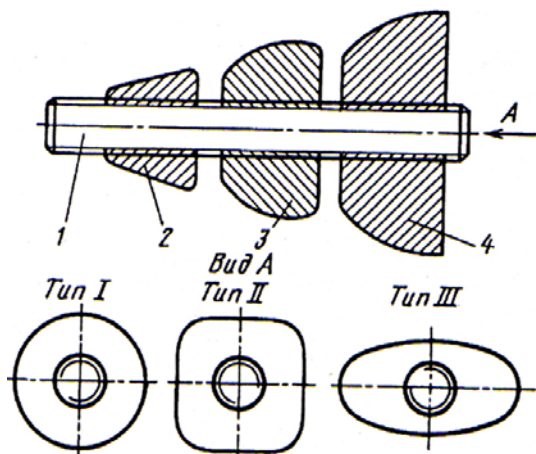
Пуансон для отбортовки фланцев в стенке трубной заготовки
